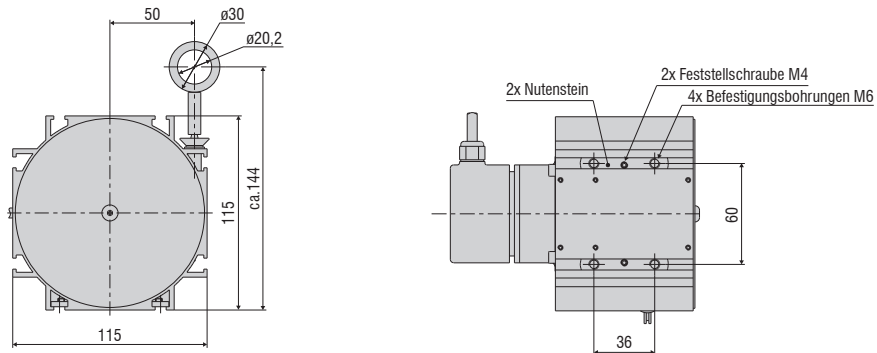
Maßzeichnung WDS- ... - P115 - XX - XXX, Abmessungen in mm
